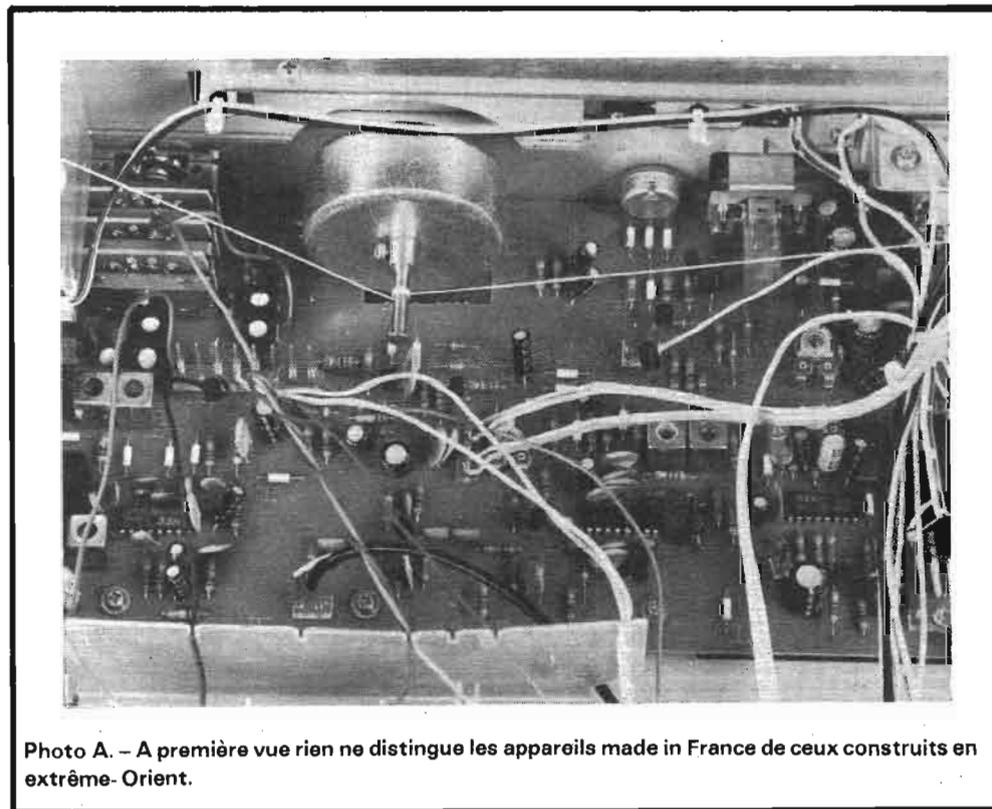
Photo A. - A première vue rien ne distingue les appareils made in France de ceux construits en extrême-Orient.
